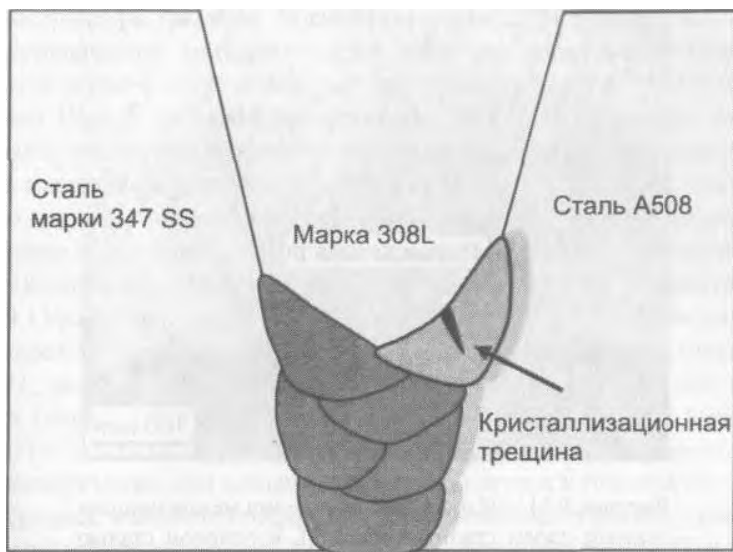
Кристаллизационная трещина в сварном шве разнородного соединения из нержавеющей стали марки 347 и стали марки A508 для изготовления сосудов давления с использованием присадочного металла марки 308 L
